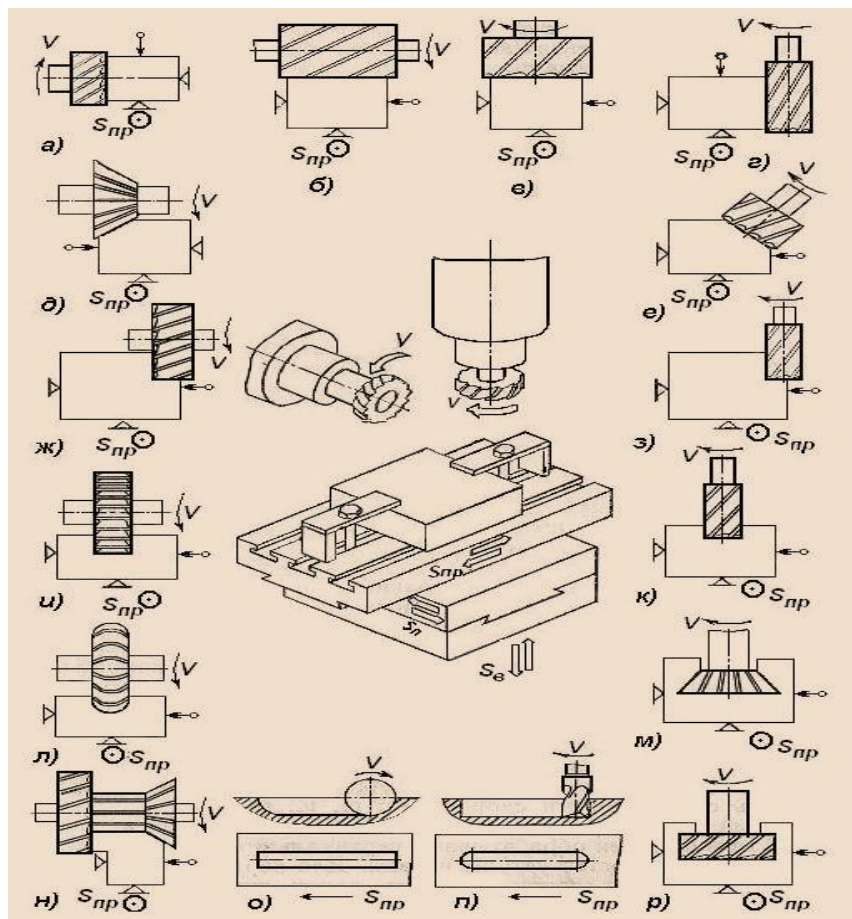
Типы фрез и схемы обработки поверхностей на фрезерных станках:
